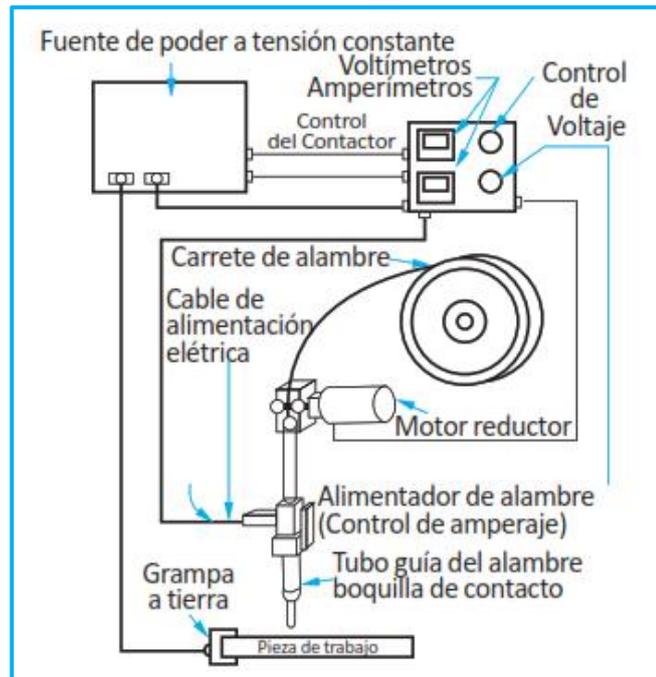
Esquema del Circuito de Soldadura con Alambre Tubular
